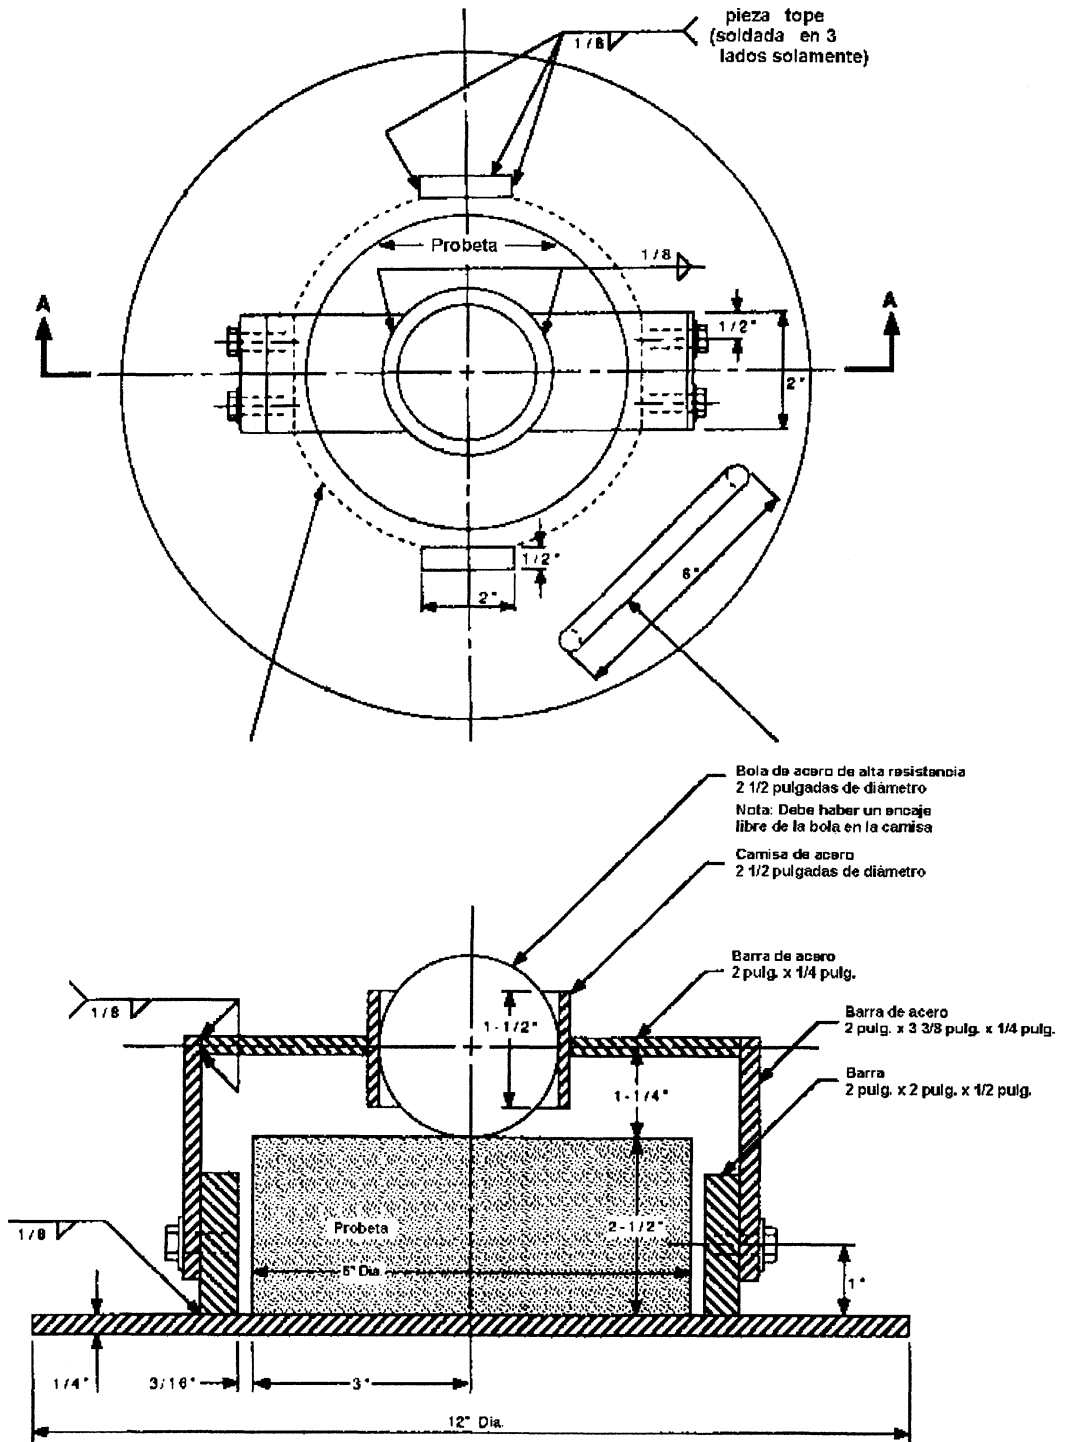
Esquema del equipo para el ensayo de impacto por caída libre.
